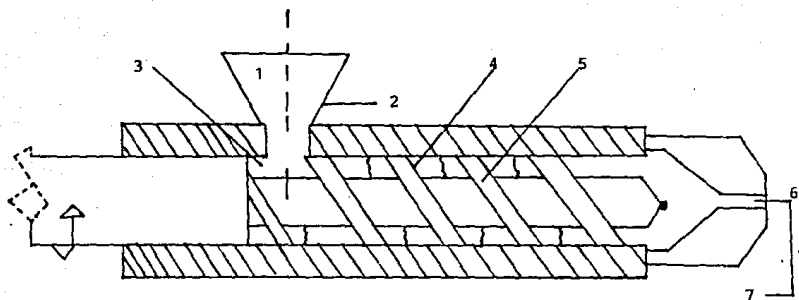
INYECTORA A HUSILLO-PISTON. 1.- Tolva de alimentacion. 2.- Deposito de resina. 3.- Zona de calentamiento y compresion. 4.- Zona de plastificacion. 5.- Husillo o tornillo sinfin. 6.- Boquilla. 7.- Molde.
